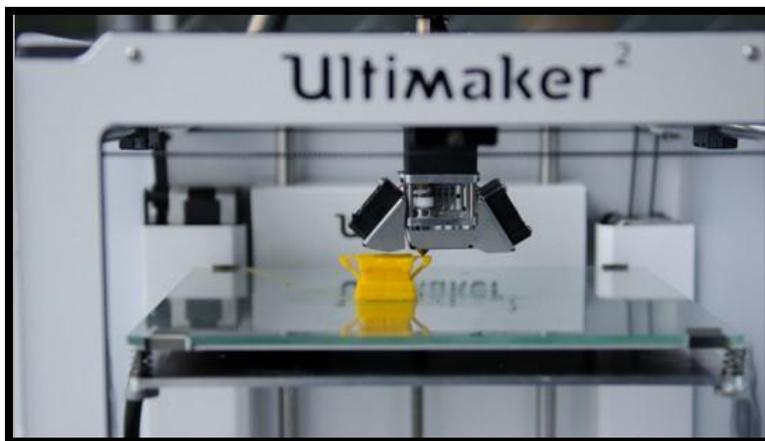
Proceso de impresión 3D, impresora Ultimaker2®
